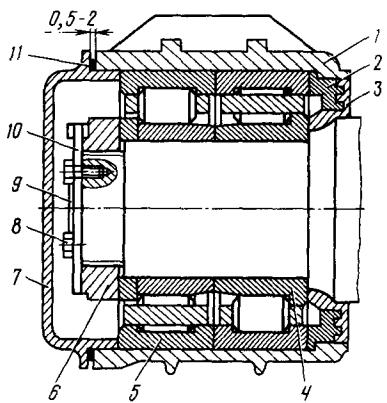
Букса с двумя цилиндрическими подшипниками на горячей посадке с торцовым креплением гайкой:
